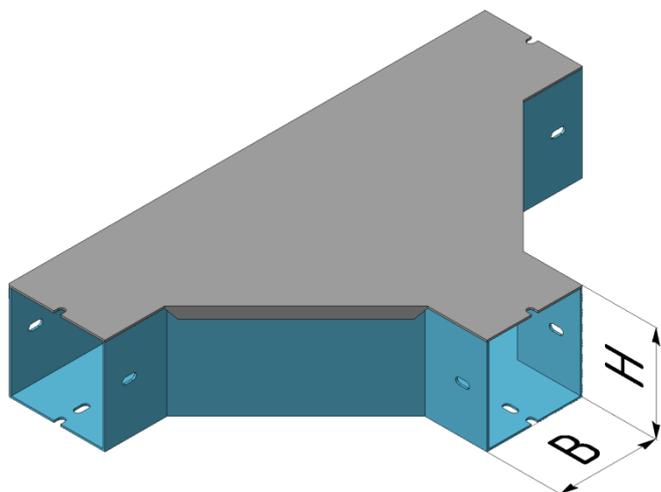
Короб угловой на три направления типа КТ. Общий вид
